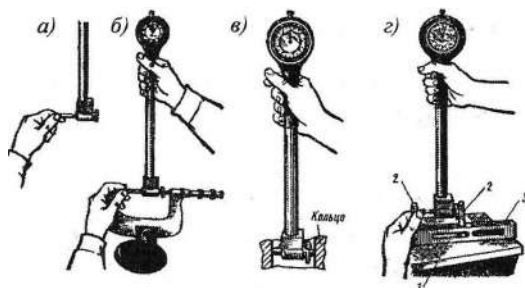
Подготовка индикаторного нутромера к работе: а — установка сменного стержня; б — проверка размера по микрометру; в — проверка размера по аттестованному кольцу; г — установка размера по блоку концевых мер (1 — блок концевых мер, 2 — боковики, 3 — державка) [10, с. 221]
